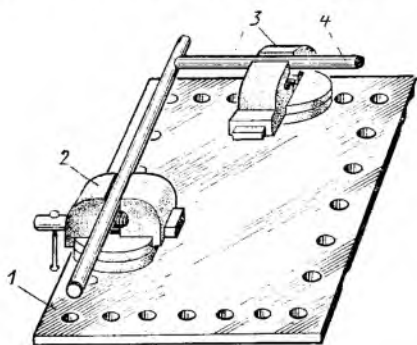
Крепление труб под требуемым углом для сварки
